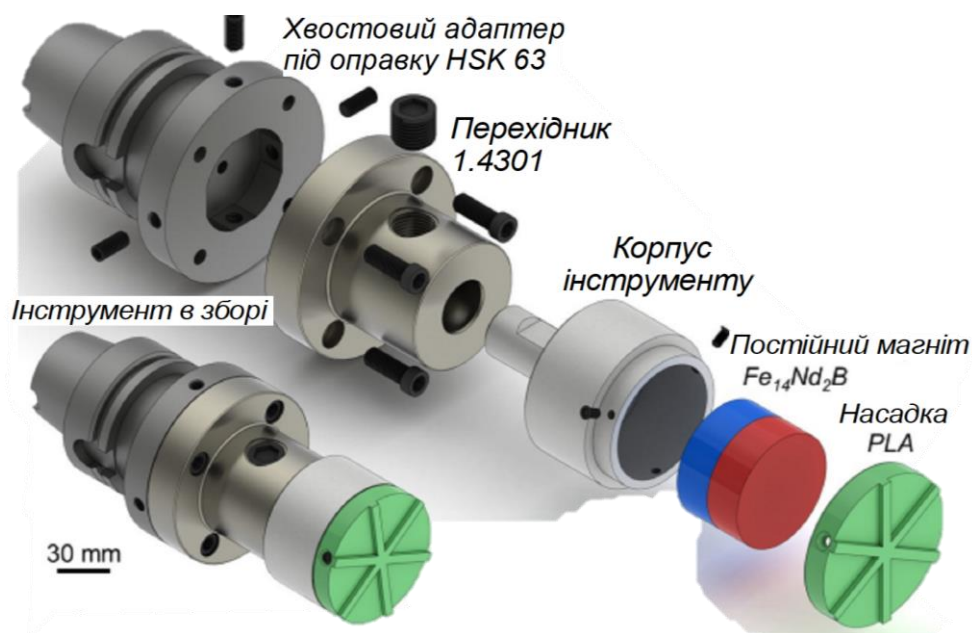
Конструкція магнітно-абразивного інструмента
